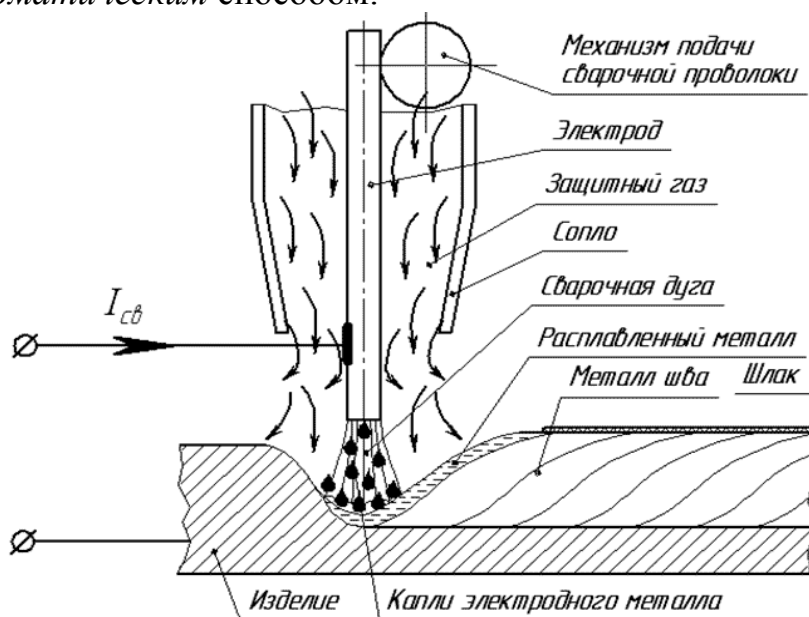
Схема аргонодуговой сварки плавящимся электродом
